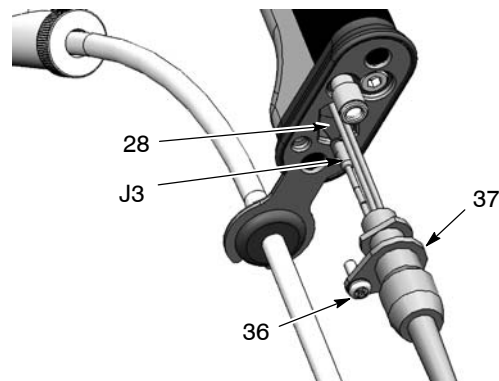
Dépose du capuchon pneumatique et du tube à poudre
